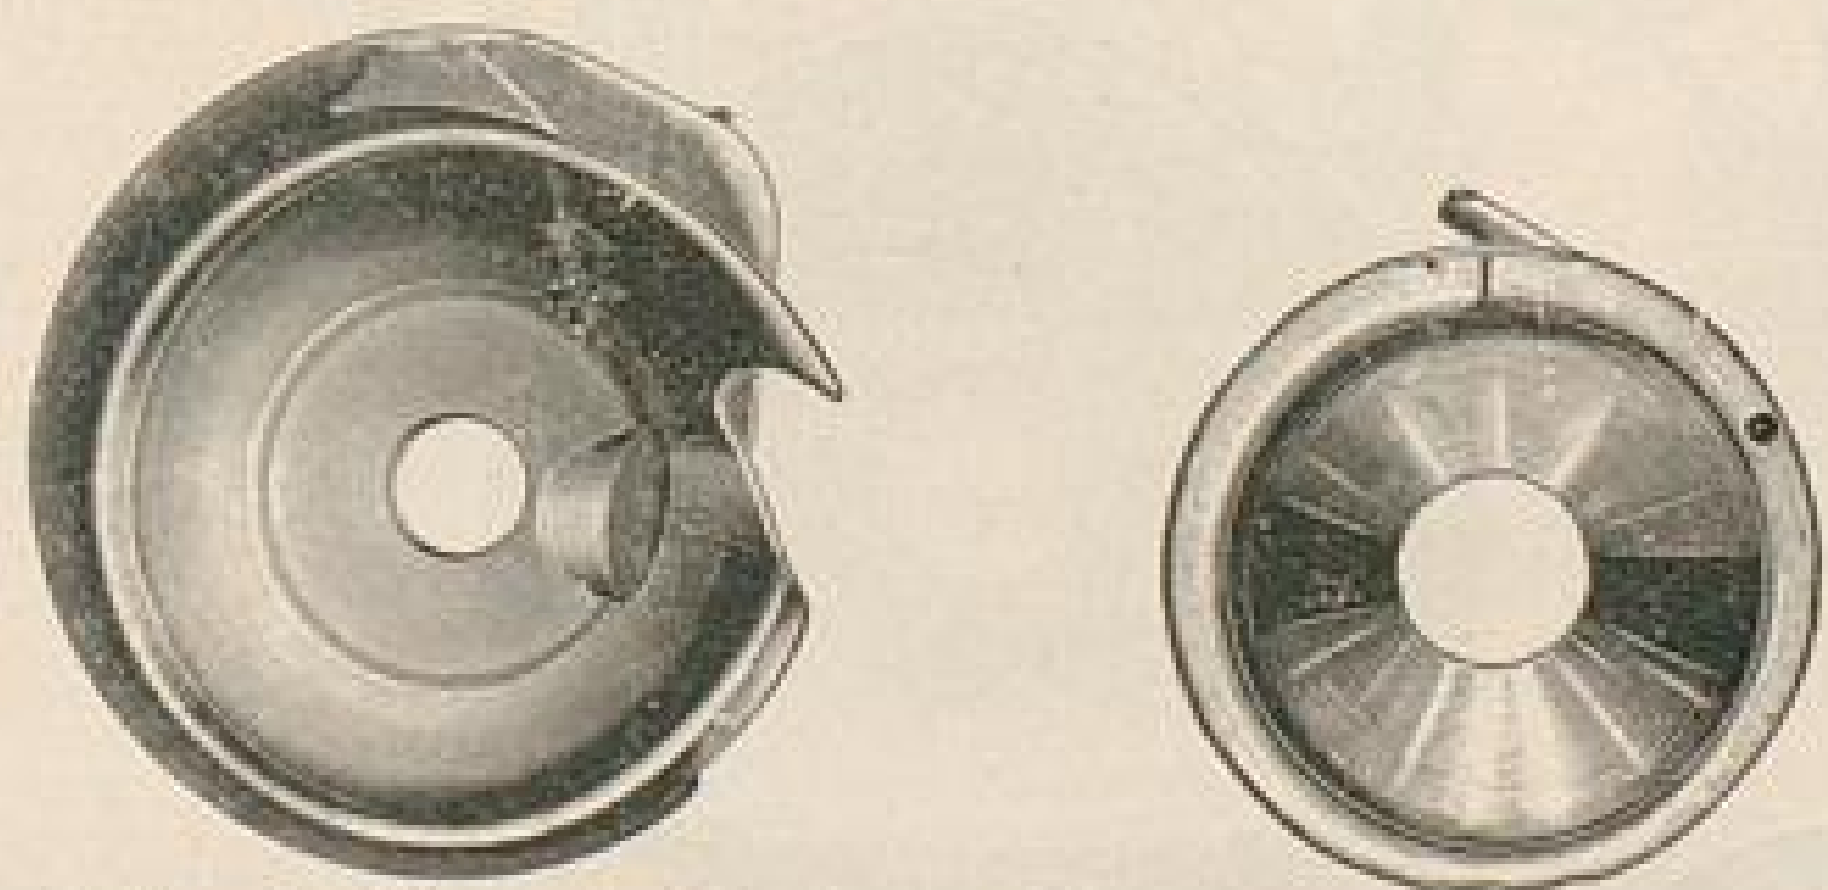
Greifser und Spulenkapsel der Maschinen mit Brille.
